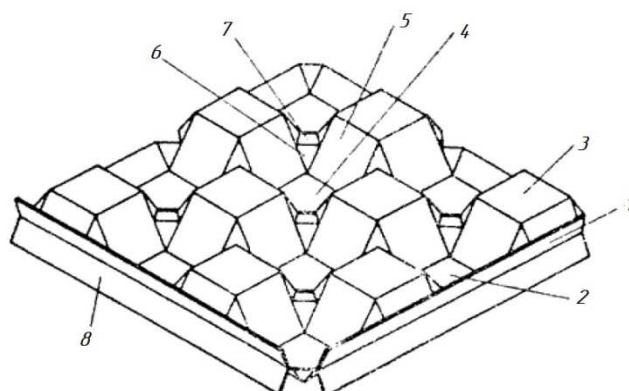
прокладка для транспортировки и хранения плодов в ящиках (А.С. № 1706932): 1 – многогранная плита, 2 – углубления, 3 – выступы, 4 – горизонтальная прямоугольная грань, 5 – прямоугольная наклонная боковая грань, 6 – треугольная наклонная грань, 7 – квадратное вентиляционное отверстие, 8 – полоска.
